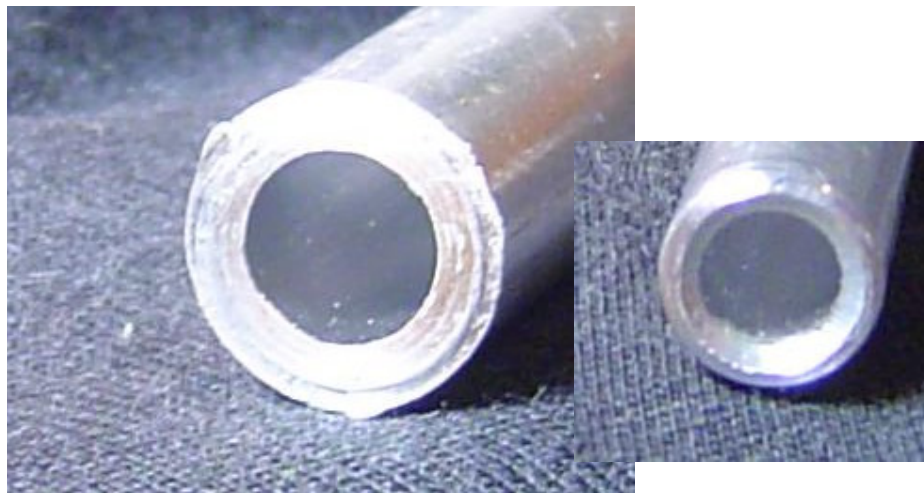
Superfície após o corte (esquerda) e com acabamento (direita)
